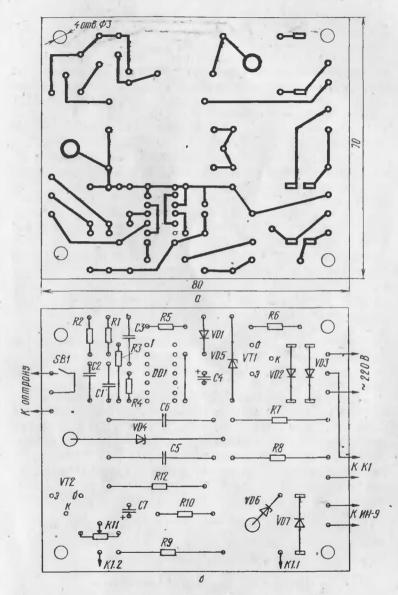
Чертеж печатной платы блока «Сеть»: a — вид со стороны токопроводящих дорожек; <math>b — co стороны деталей
